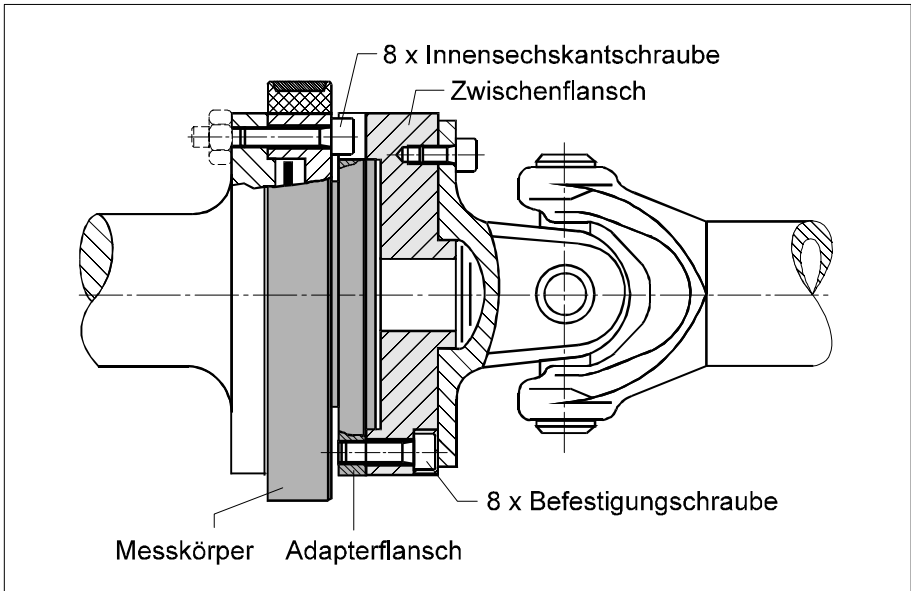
Verschraubung des Rotors beim Drehmoment-Messflansch T10F
